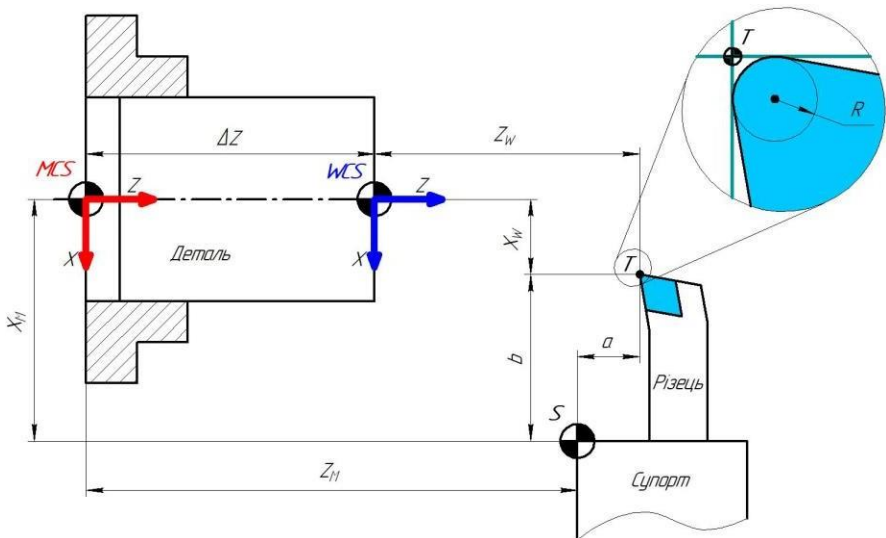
Система координат токарного верстата з ЧПК
